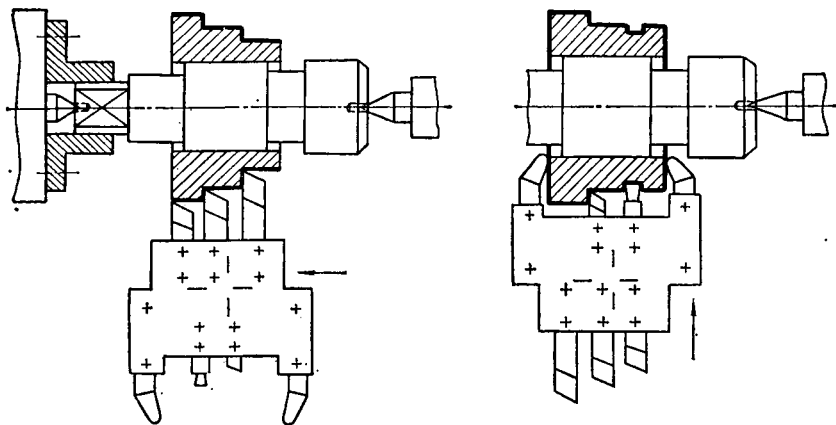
Специальные поворотные резцедержатели для токарных станков
